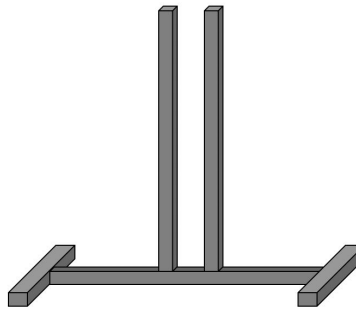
Structure schématique construite à partir de pièces Norcan. Les deux barres disposées à terre de part et d'autre de la barre horizontale principale servent à assurer une meilleure stabilité.
